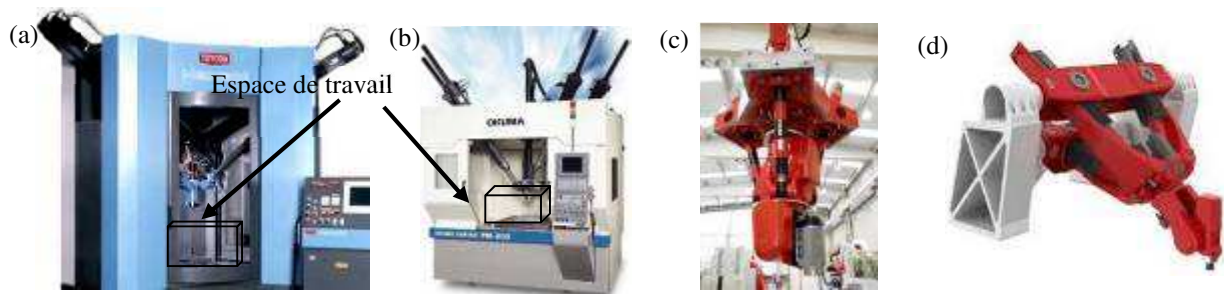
Machines-outils parallèles d'usinage : HexaM de TOYODA (a) et cosmo center PM-600 de OKUMA(b), Architecture hybride d'usinage : PKM Tricept(c), Exechon(d)
